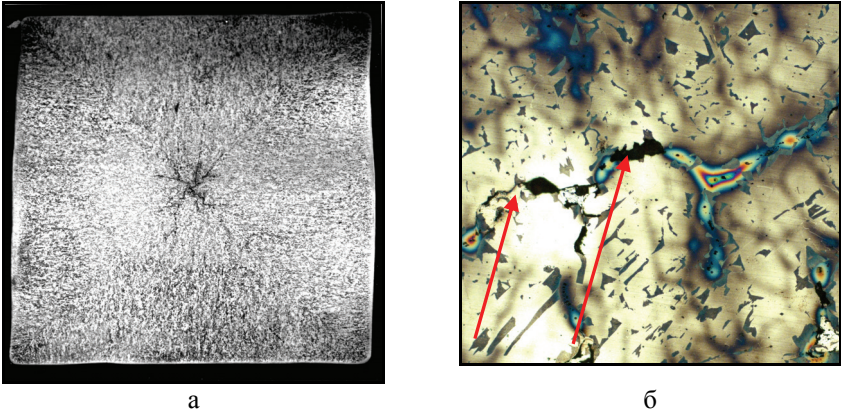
Трещины в непрерывнолитых заготовках:
